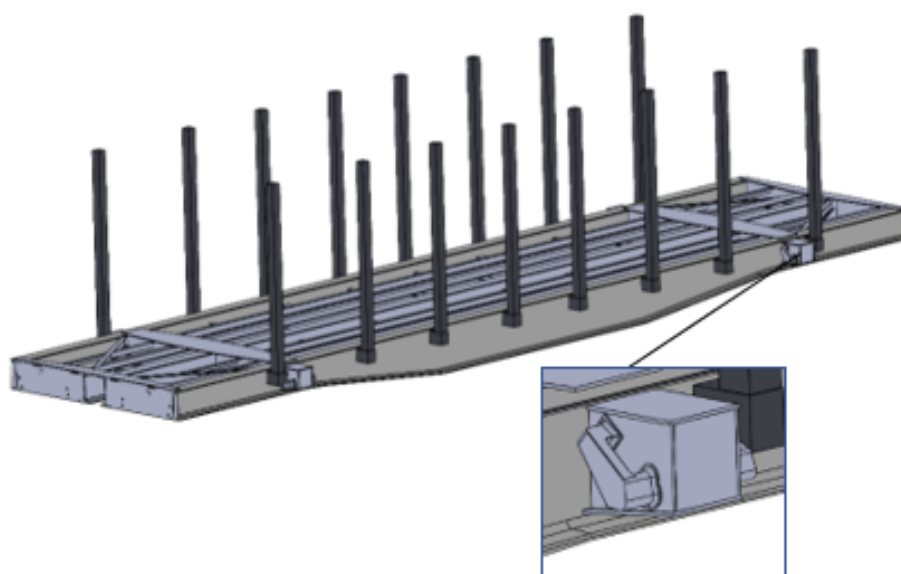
Просторова модель несучої конструкції вагона-платформи з вузлами для закріплення ланцюгових стяжок
